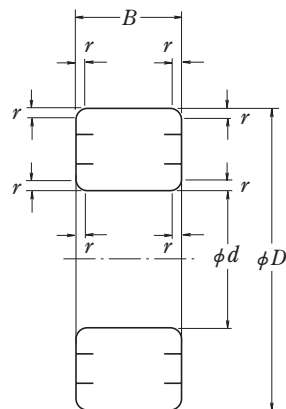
Äußere Abmessungen für Radialkugel- und -rollenlager
